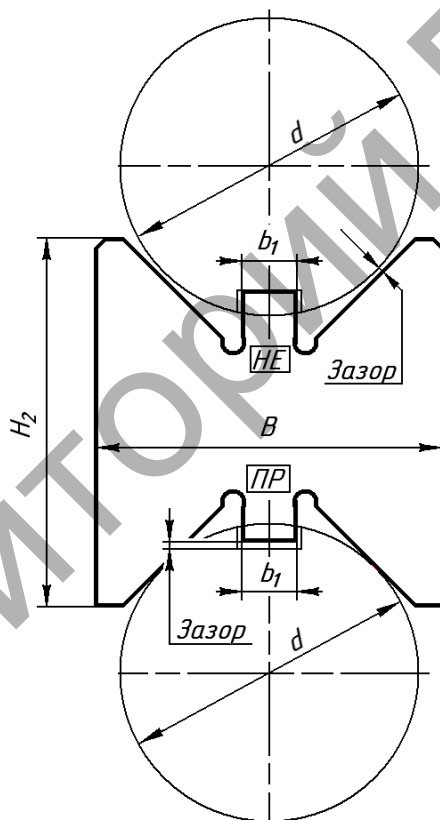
Калибр-глубиномер шпоночный для вала и методика измерения им
